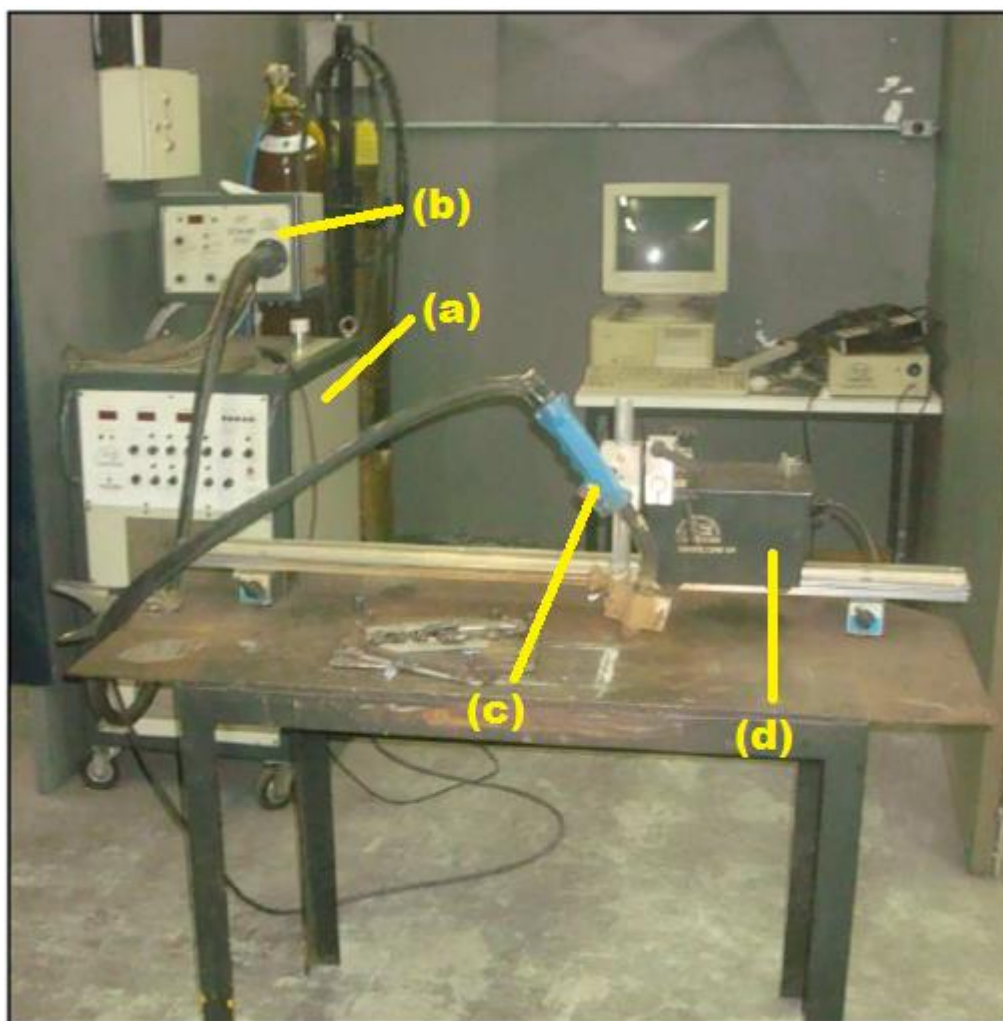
Bancada de deposição dos cordões: (a) fonte de soldagem; (b) alimentador de arame; (c) tocha de soldagem; (d) movimentador da tocha.
